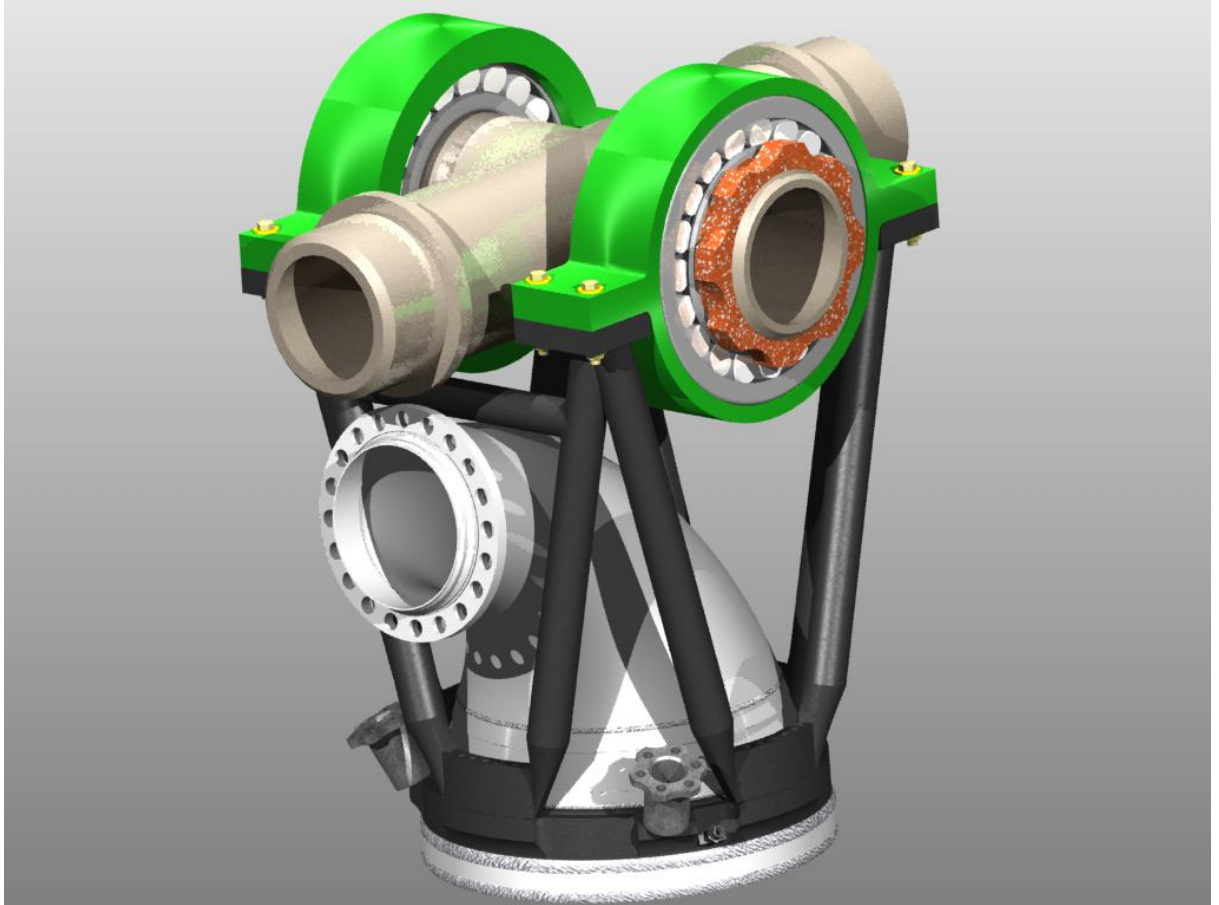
Конструкция подвижного крепления ЖРД НК-33
